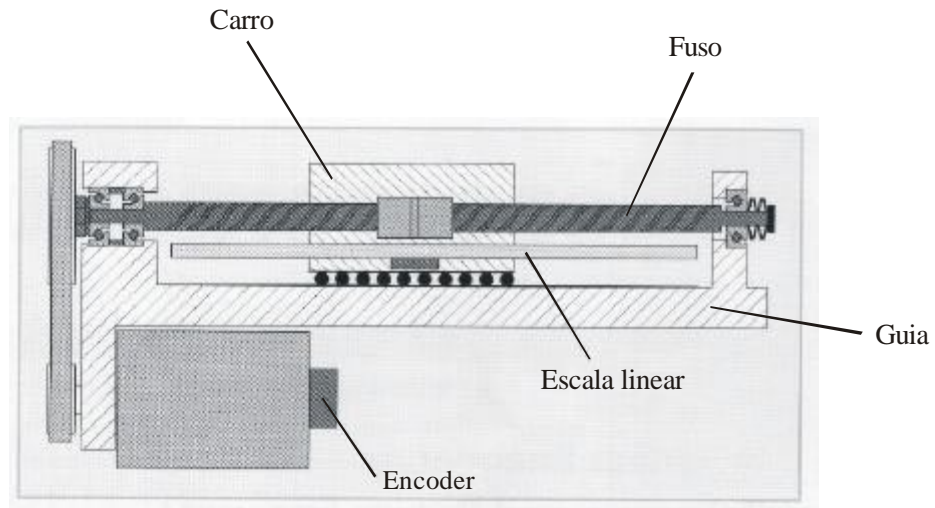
Sistemas de medição de posicionamento em máquinas-ferramenta [57]
